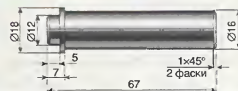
Оправка для выпрессовки внутренней втулки шарнира.
